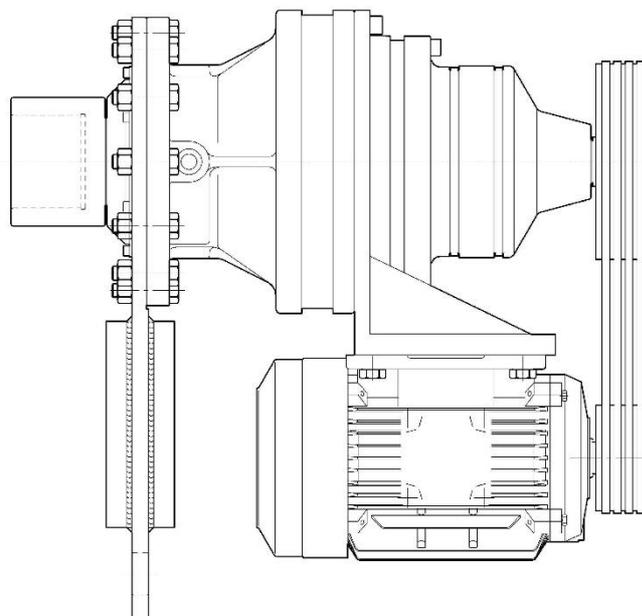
Пример установки ременного привода на вход редуктора с реактивной штангой.
